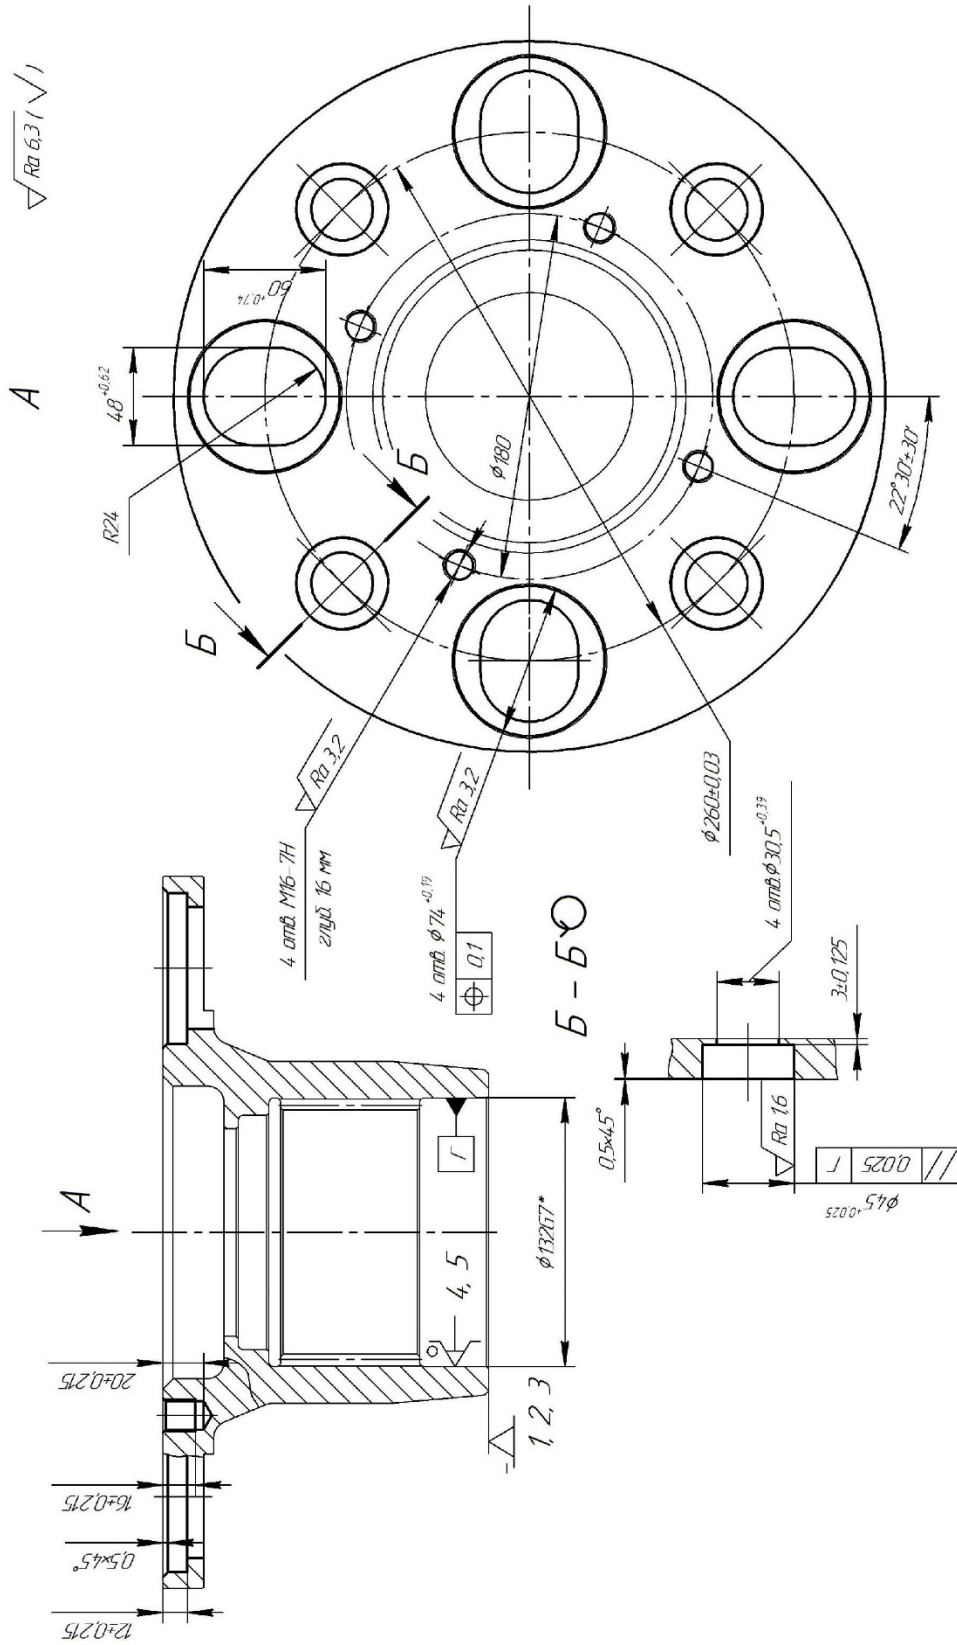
Схема базування заготовки на операції 070 комплексній на ОЦ з ЧПК
